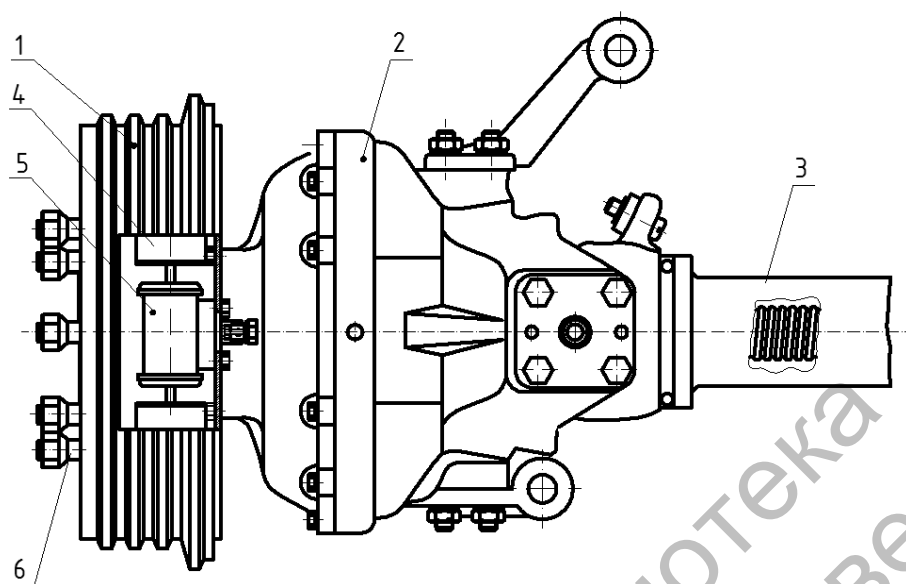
Расположение тормозного механизма передних ведущих колес трактора с неподвижными опорами относительно колесного редуктора: 1 – барабан тормозной; 2 – редуктор колесной передачи; 3 – передний ведущий мост; 4 – колодка тормозная; 5 – гидроцилиндр; 6 – болт
